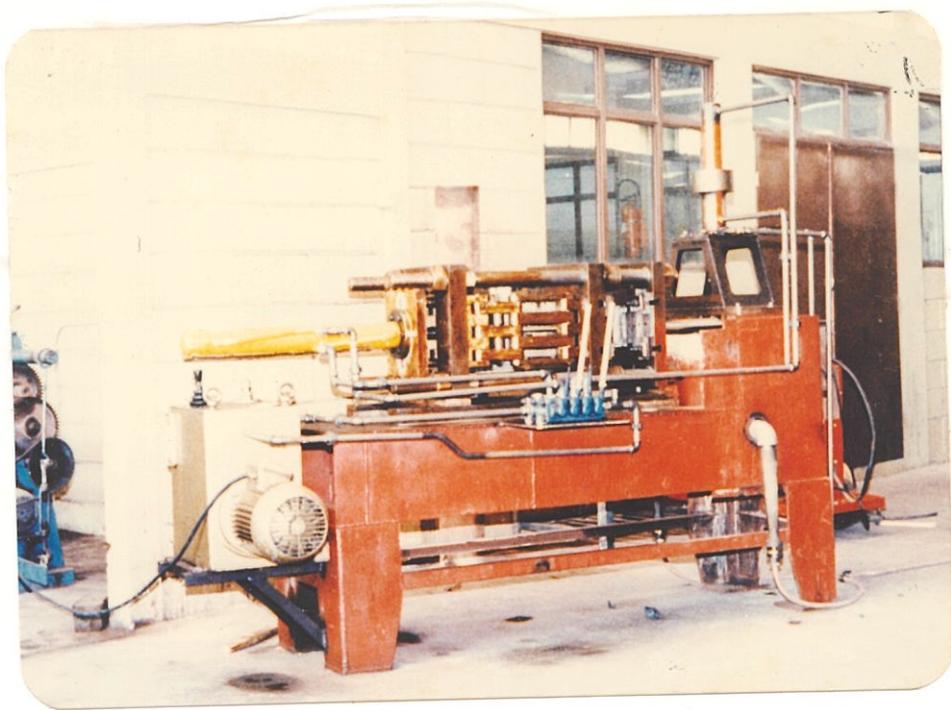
MAQUINA DE FUNDICION A PRESION FABRICADA EN LA
